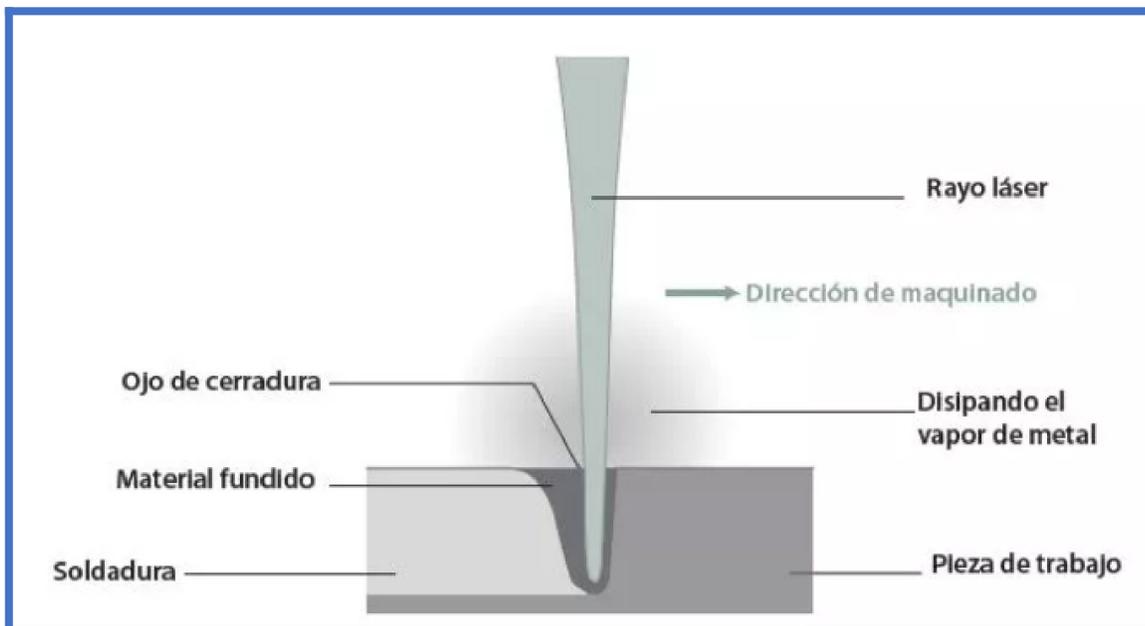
,1. La soldadura ojo de cerradura requiere densidades de potencia sumamente altas y se usa en aplicaciones que requieren soldaduras profundas. Fuente.
